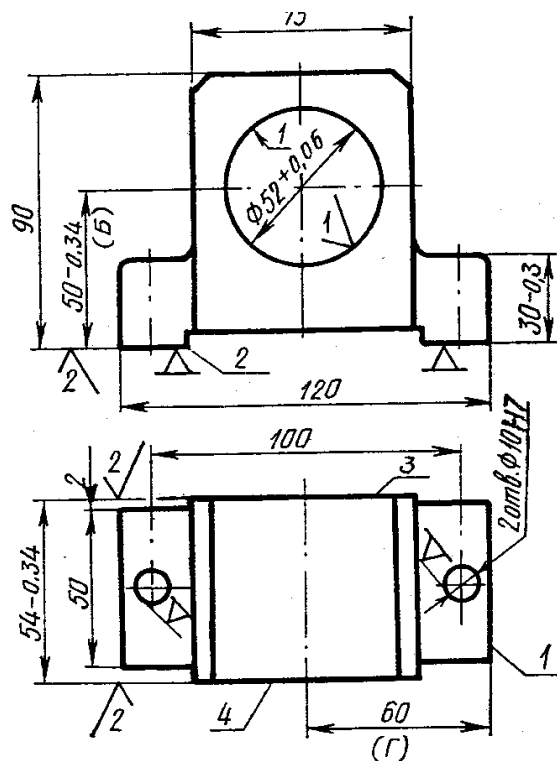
Корпус подшипника. Чертеж и схема установки при обработке отверстия  $\varnothing 52^+$
